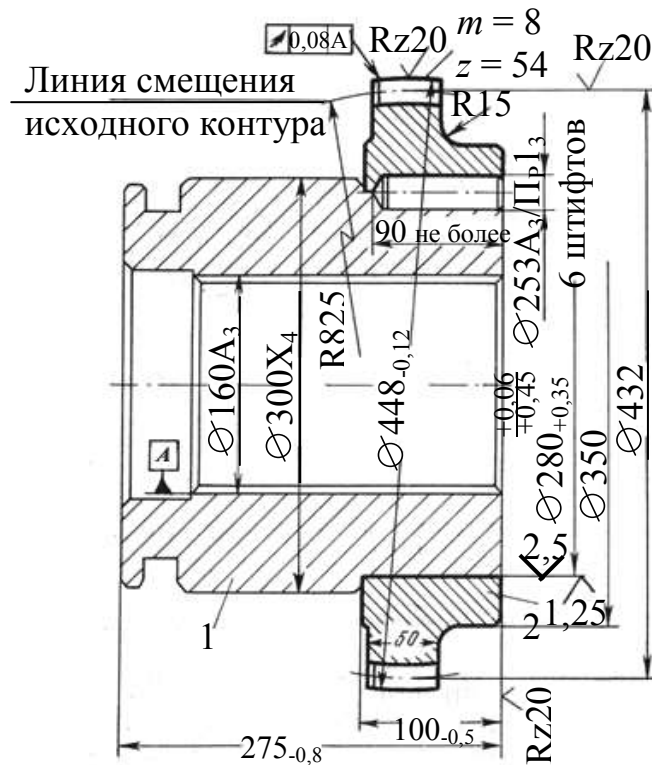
Ремонтный чертеж восстановления венца втулки зубчатой муфты: 1 – исходная деталь; 2 – ремонтный бандаж
